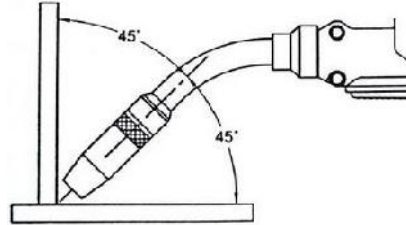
Efecto de la posición del electrodo y de la técnica de soldadura.
